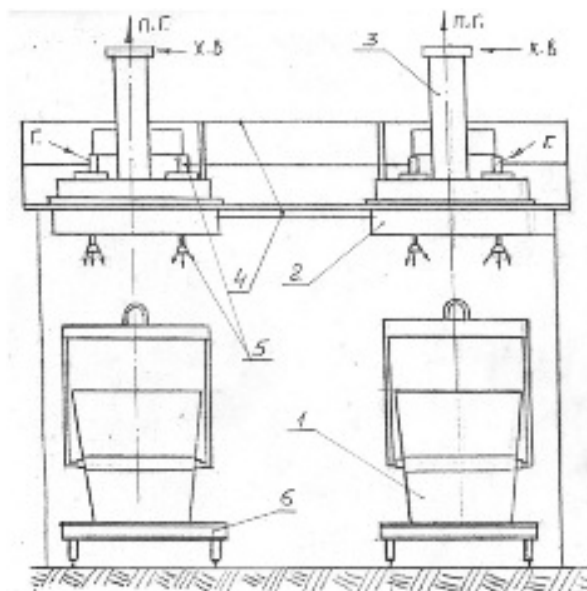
Схема двухпозиционного станда для сушки и прокаливания ковшей под цветные металлы: 1 – ковш; 2 – крышка; 3 – рекуператор; 4 – площадка; 5 – горелка; 6 – тележка с устройством вертикального перемещения ковшей до крышки
